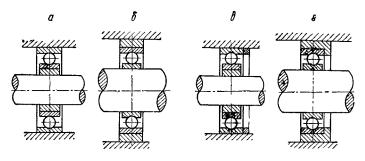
Установка шариковых и роликовых подшинников с ремонтными втулками и кольцами:
